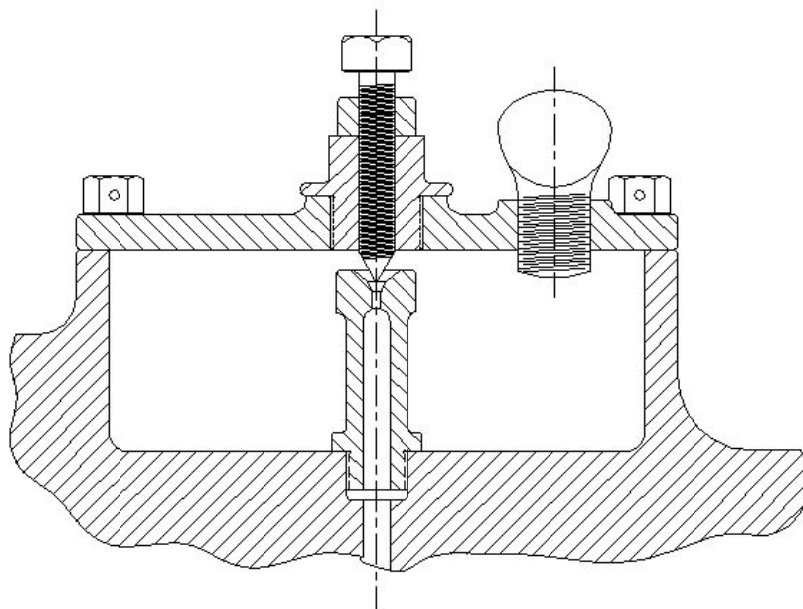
Depósito engrasador del Midi, para partes móviles del mecanismo.
